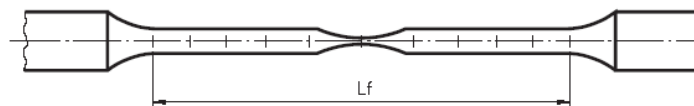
Corpo de prova para ensaio de tração depois do ensaio.
